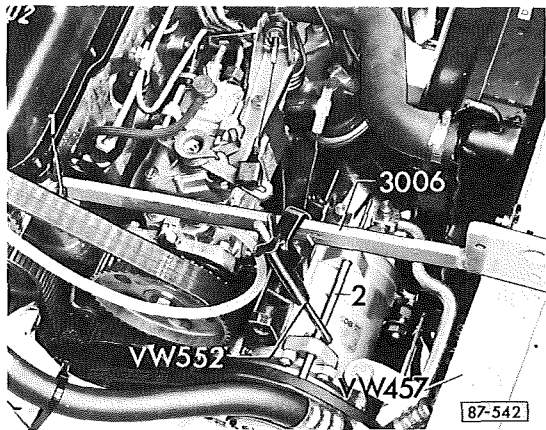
Réglage de la courroie trapézoïdale de la pompe de liquide de refroidissement et du compresseur
